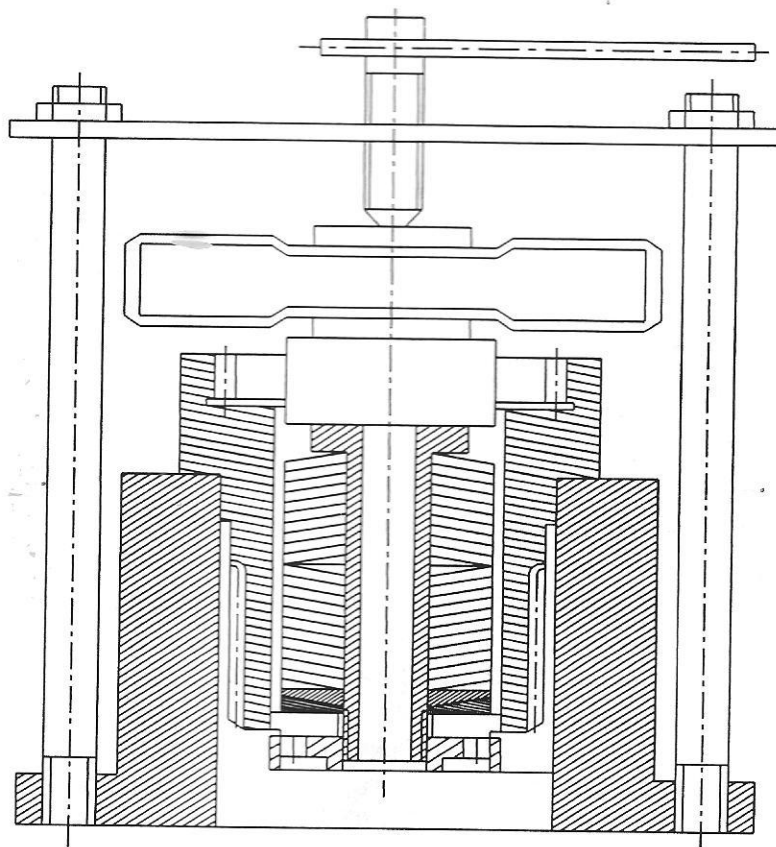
Сборочный узел для предварительного нагружения пакета тарельчатых пружин
